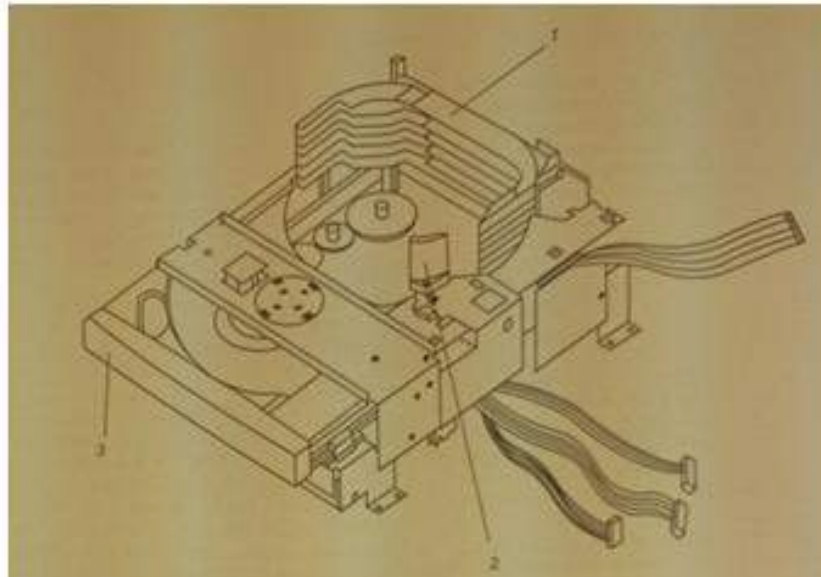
Конструкция механизма загрузки проигрывателя компакт-дисков музыкального центра Hitachi AX-SB
